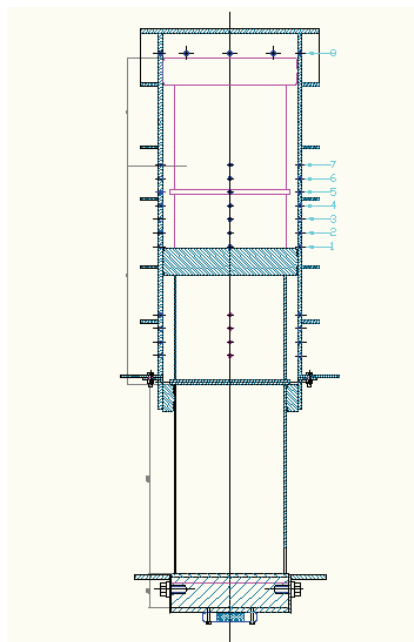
Вид поршневого демпфера в сборе со штатным расположением калиброванных отверстий
